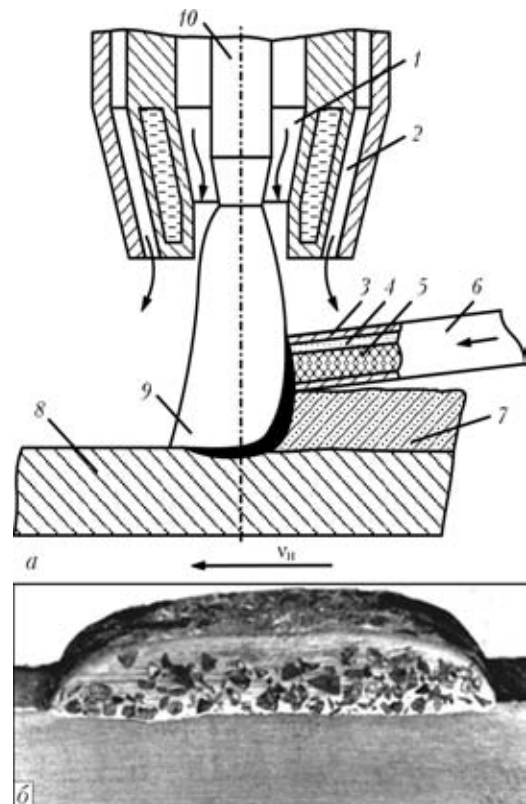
Схема плазменной наплавки композиционных сплавов с использованием в качестве присадочного материала ленточного релита (а) (1, 2 — соответственно плазмообразующий и защитный газ; 3 — оболочка; 4 — мелкодисперсная шихта; 5 — армирующие частицы; 6 — присадочный материал; 7 — наплавленный слой; 8 — образец; 9 — столб плазменной дуги; 10 — электрод) и макрошлиф наплавленного валика (б)
